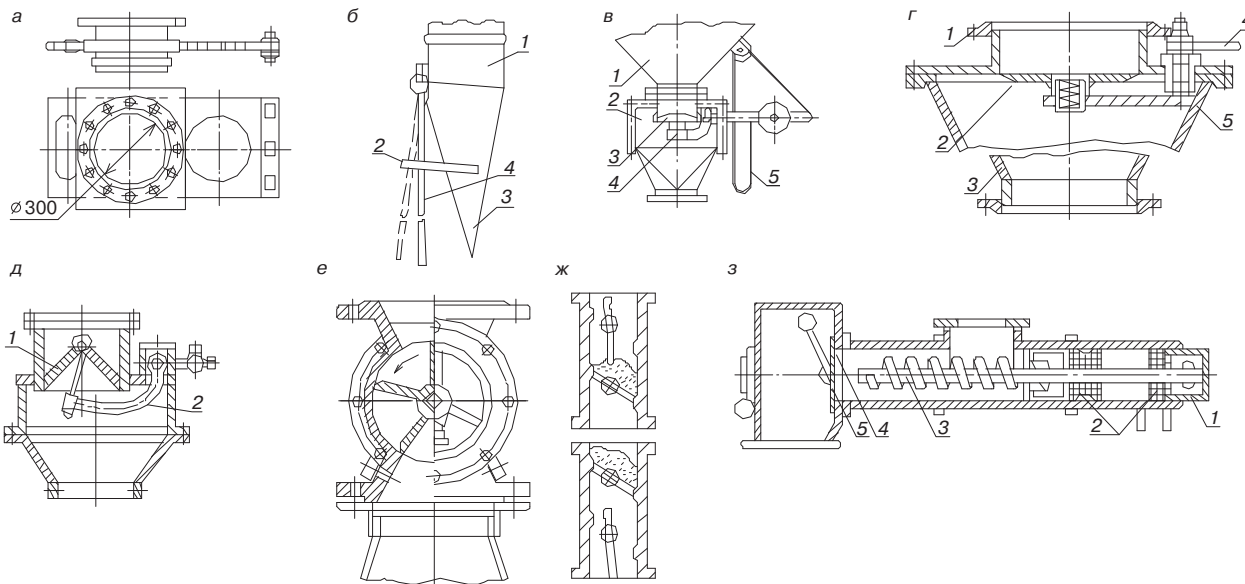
Схемы устройства пылевых затворов: а – шиберный затвор обычный; б – дисковый затвор: 1 – верхняя часть корпуса; 2 – диск-заслонка; 3 – нижняя часть корпуса; 4 – рукоятка; в – клапанный затвор: 1 – бункер; 2 – корпус; 3 – клапан; 4 – рычаг; 5 – канат; г – плоская мигалка: 1 – стояк; 2 – язык; 3 – ограничитель; 4 – петля; 5 – корпус; д – мигалка с конусным клапаном: 1 – клапан; 2 – рычаг с грузом; е – шлюзовой питатель роторного типа с электроприводом; ж – двойной пылевой затвор Гипрогазоочистки с электроприводом; з – винтовой затвор с пылевой пробкой: 1 – винт; 2 – опора; 3 – шнек; 4 – клапан; 5 – груз
